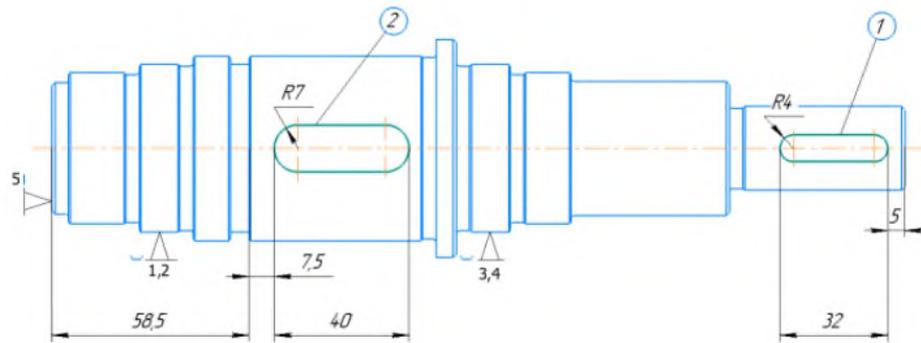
Схема базування заготовки при фрезеруванні шпонкового пазу 035
